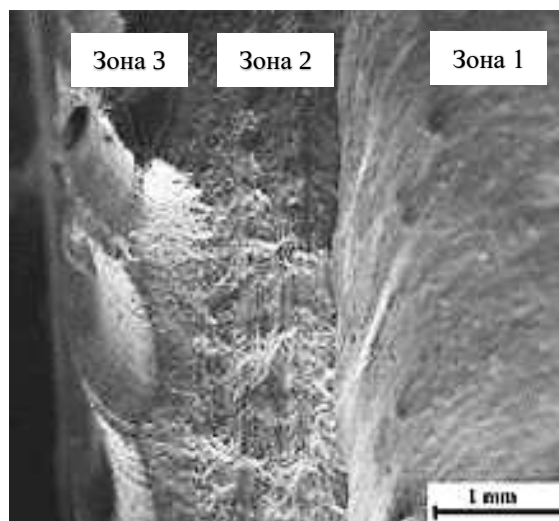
Рельеф поверхности разрушения сварного соединения, выполненного методом сварки трением с перемешиванием
